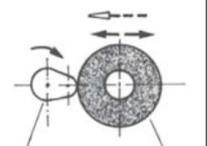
Universal-Rundschleifmaschine; Quelle: Buderus
